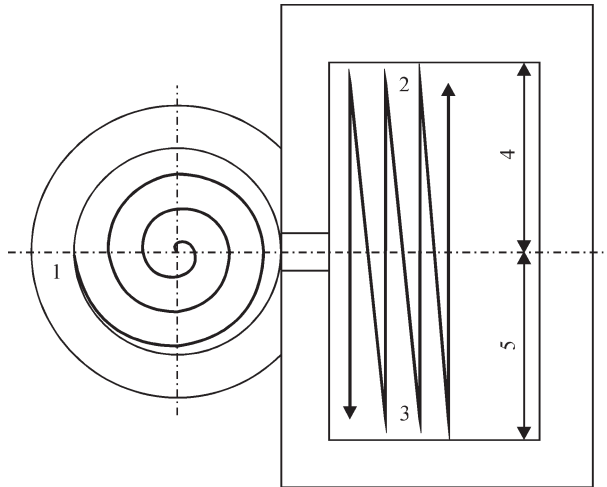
Схема розташування розгортки променів для плавки зливок сплавів титану
